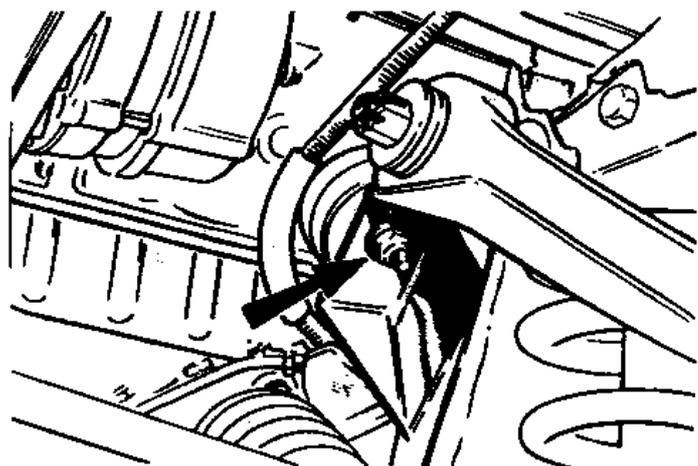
Отверните гайку левого узла крепления двигателя (Разд.33)
